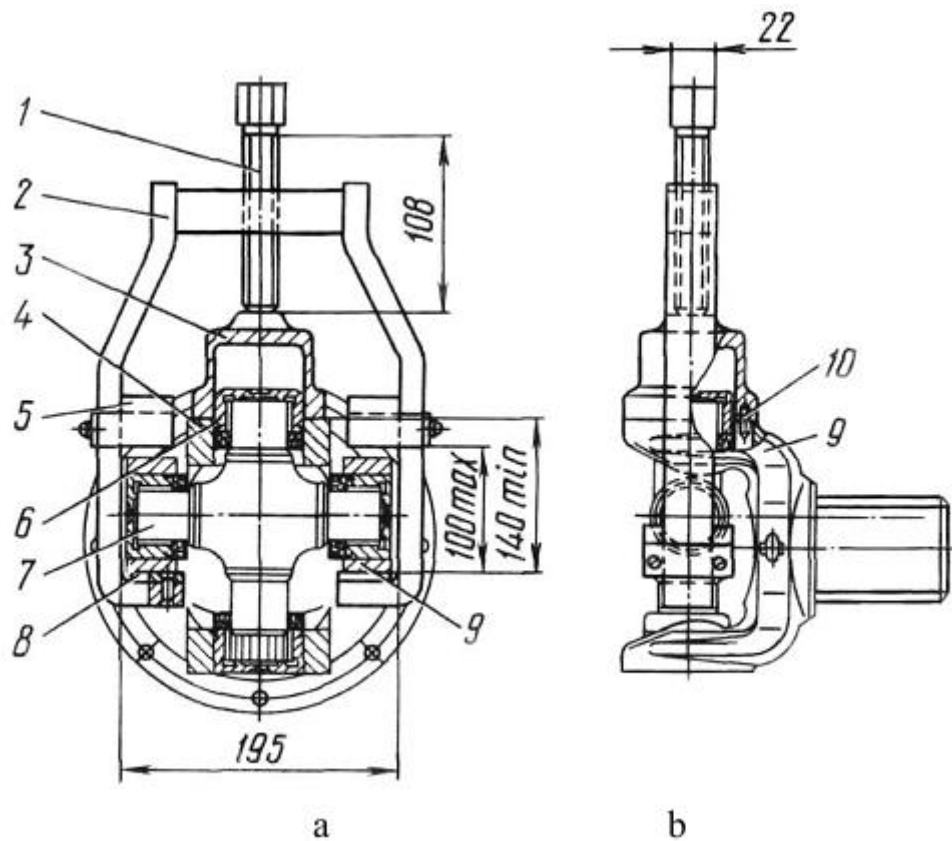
Випресування підшипників хрестовини карданного валу:
